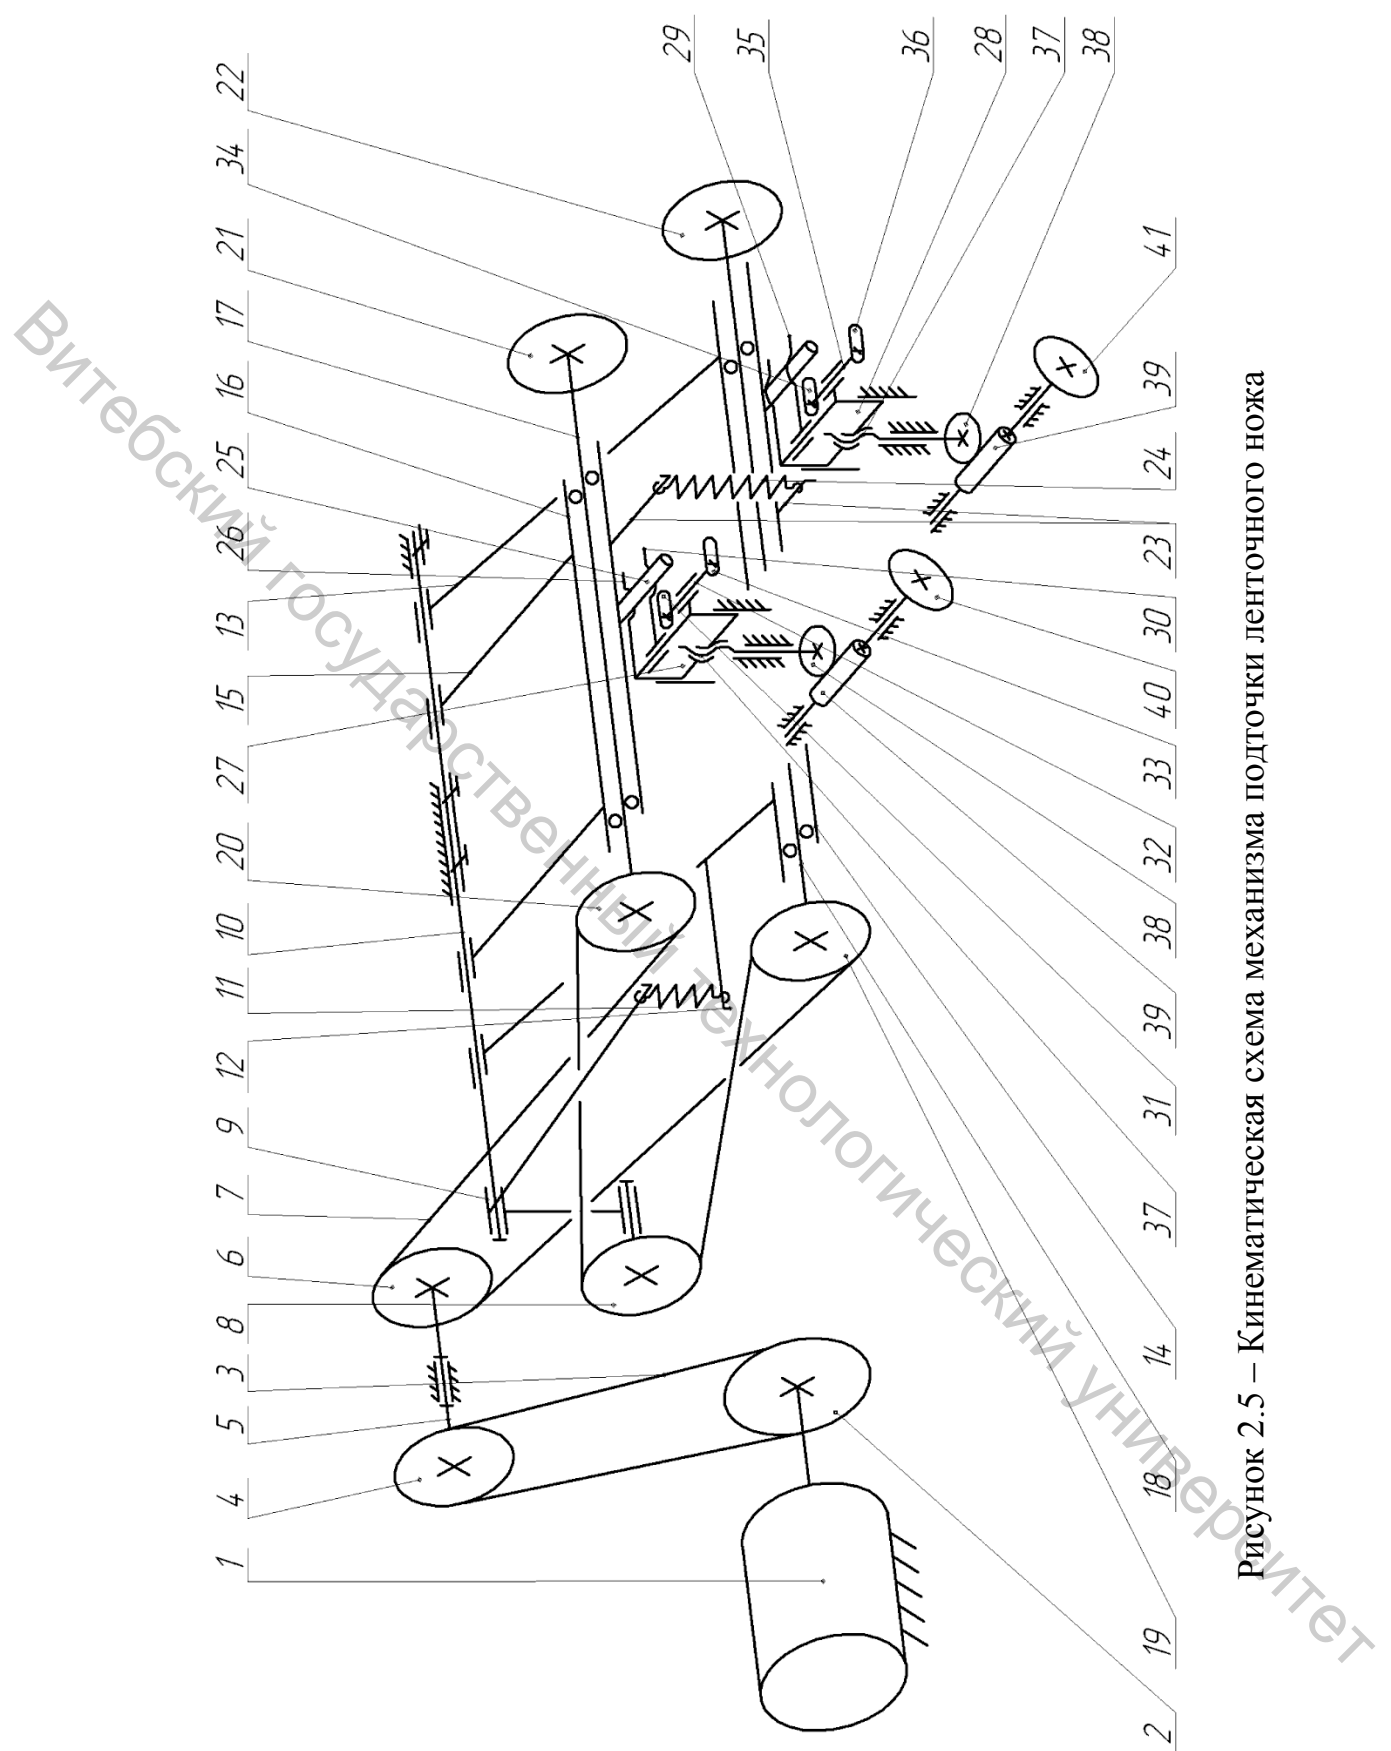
Кинематическая схема механизма подточки ленточного ножа
